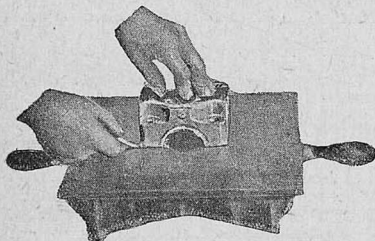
Проверка плоскости соединения половинки подшипника по проверочной плите
